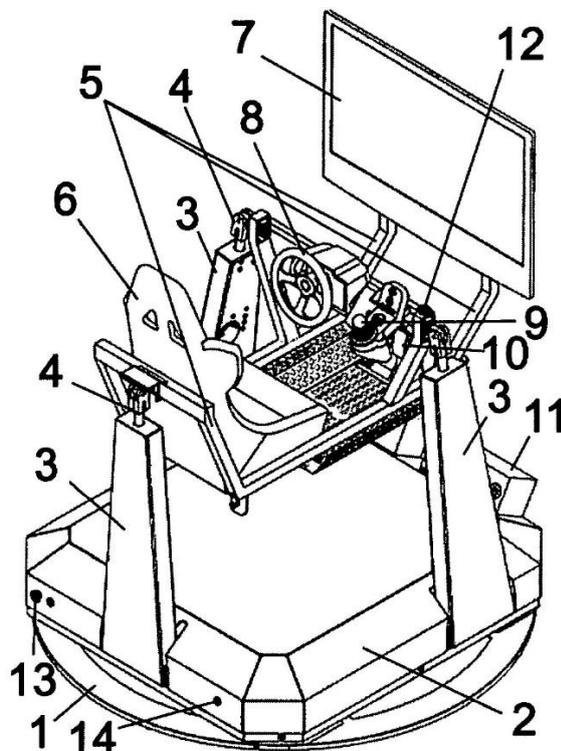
Общий вид конструкции [47]
